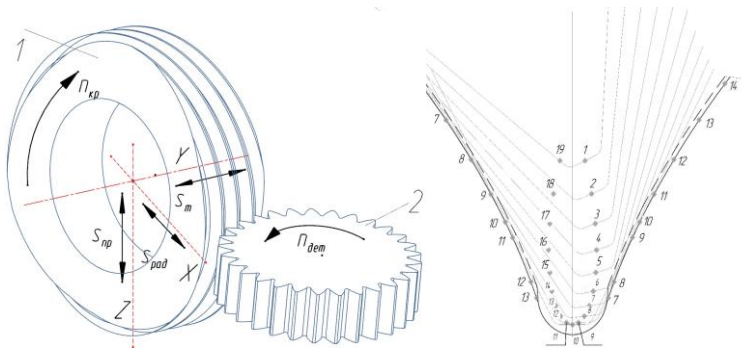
Модель движения непрерывного обкатного зубошлифования червячным кругом и формирования профиля зуба
